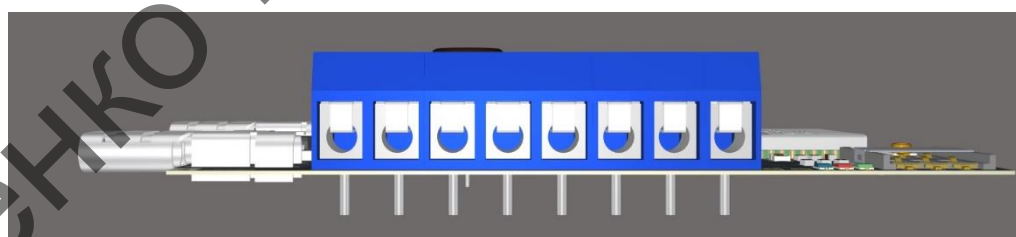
3D модель вигляд зі сторони клем
